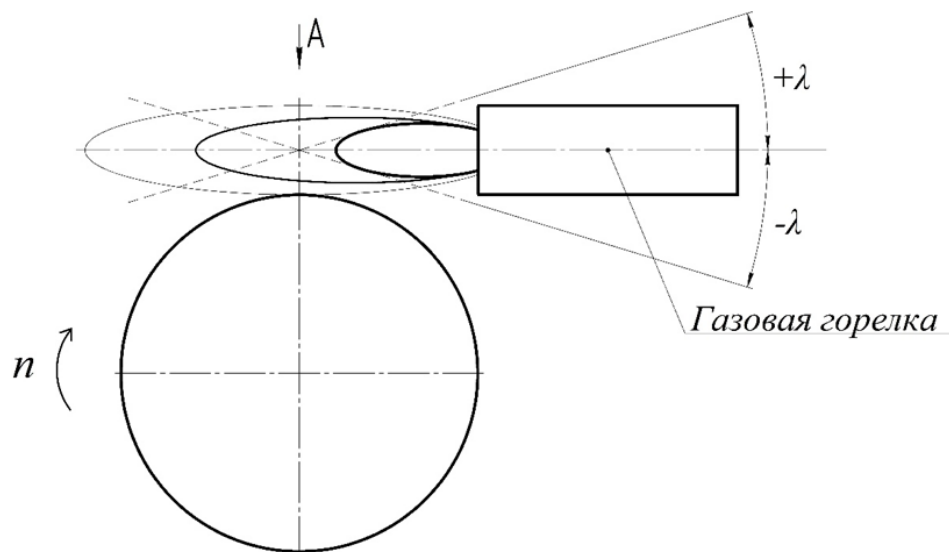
Способ дробления стружки на предварительном нагреве поверхности заготовки пламенем газовой горелки [55]
